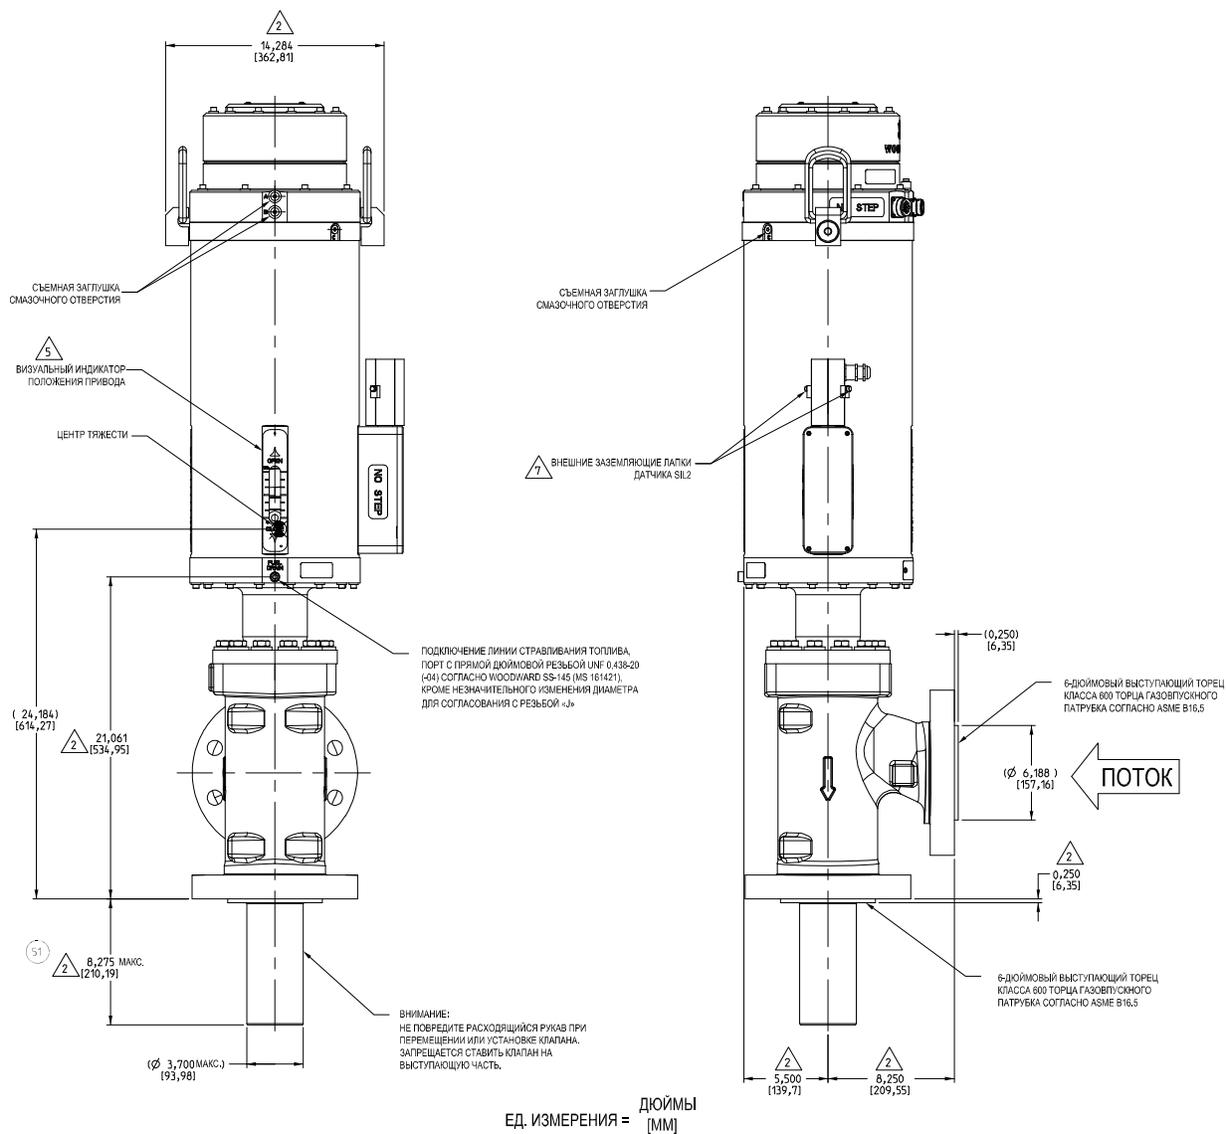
а. Габаритный чертеж (4-дюймовый клапан LESV II класса 600)
